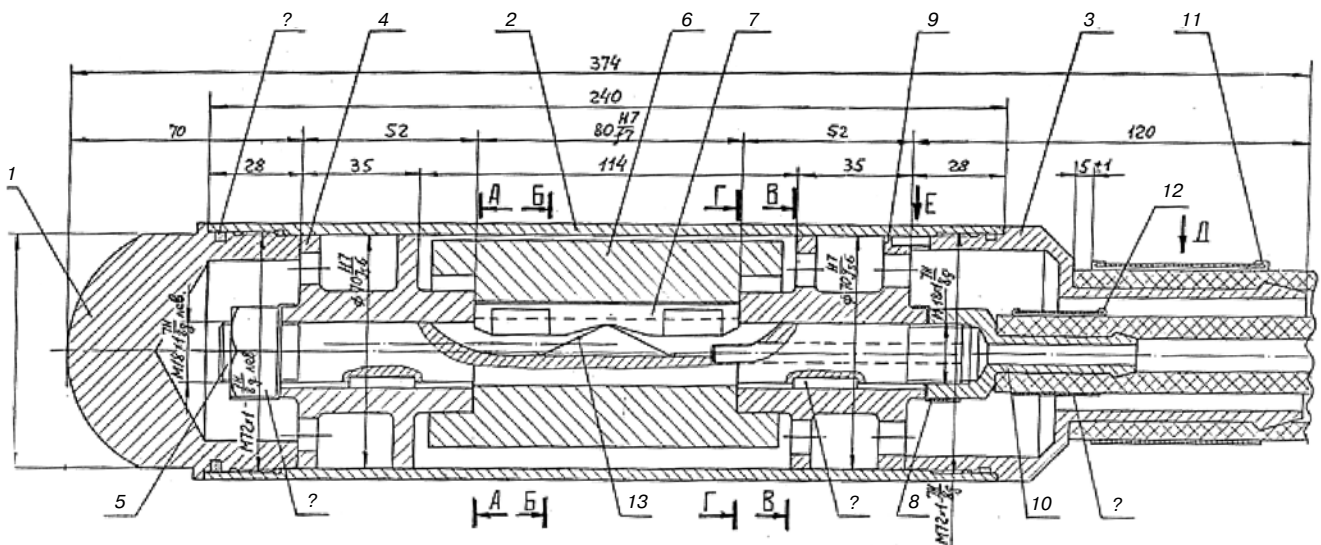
Разрез глубинного пневматического вибратора $\varnothing 77$ мм: 1 – оголовок; 2 – корпус; 3, 10 – ниппель; 4, 9 – крышки; 5 – ось; 6 – бегунок; 7 – лопатка (текстолитовая); 8 – шайба; 11, 12 – скрепка; 13 – пружина; 14 (16) – ?; 15 (17) – ?; 16 (19) – ?; 17 (22) – ?
